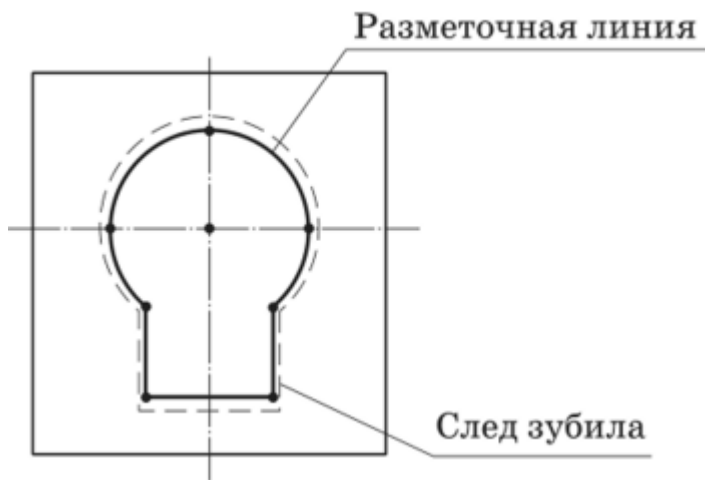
Разметка заготовки из листового металла при рубке на плите
